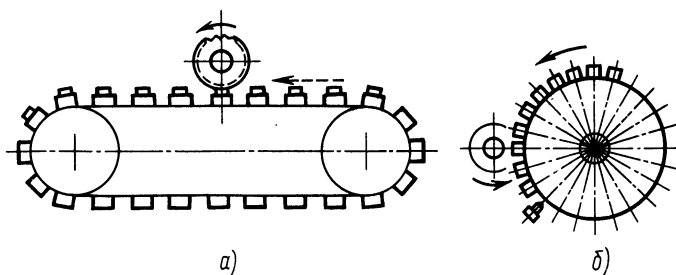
Приспособления к горизонтально-фрезерному станку:
